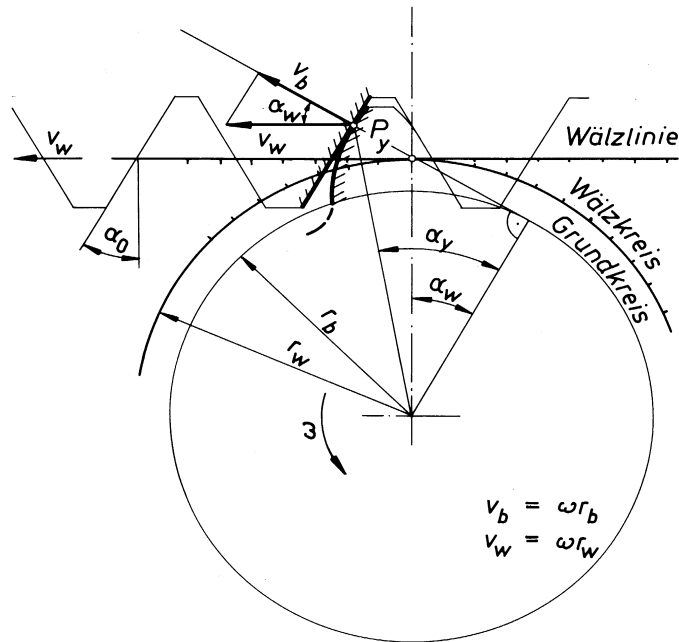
/3 a) Erzeugung der Evolvente mit einer Zahnstange als erzeugendes Werkzeug
